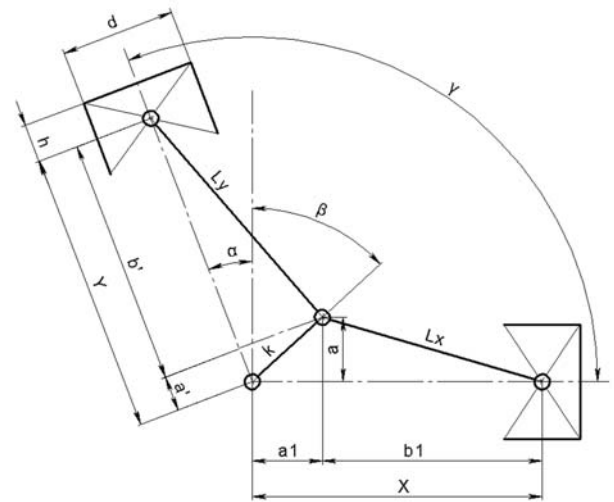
Кинематическая схема двигателя Стирлинга типа «Альфа» со свободным углом между осями цилиндров и различными длинами шатунов:
